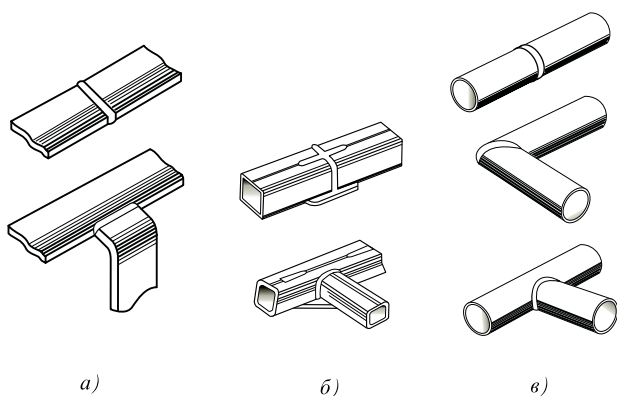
Сварные соединения шин с прямоугольным (а), коробчатым (б) и трубчатым (в) профилями
